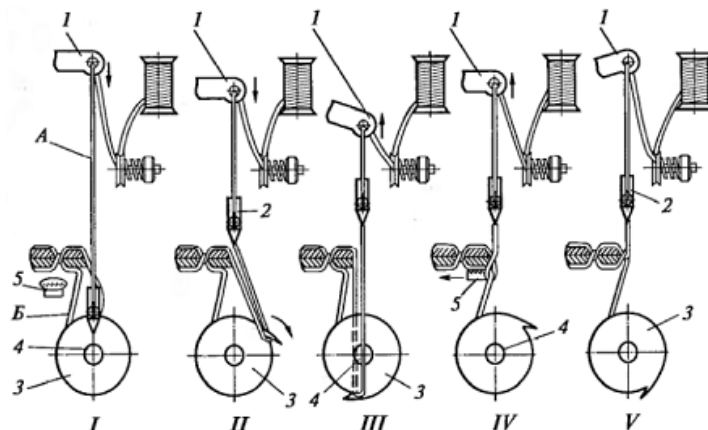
Основные фазы процесса образования челночного стежка А — верхняя (игольная) нить; Б — нижняя (челночная) нить; 1 — нитепритягиватель; 2 — игла; 3 — челнок; 4 — шпуля; 5 — зубчатая рейка механизма транспортирования
